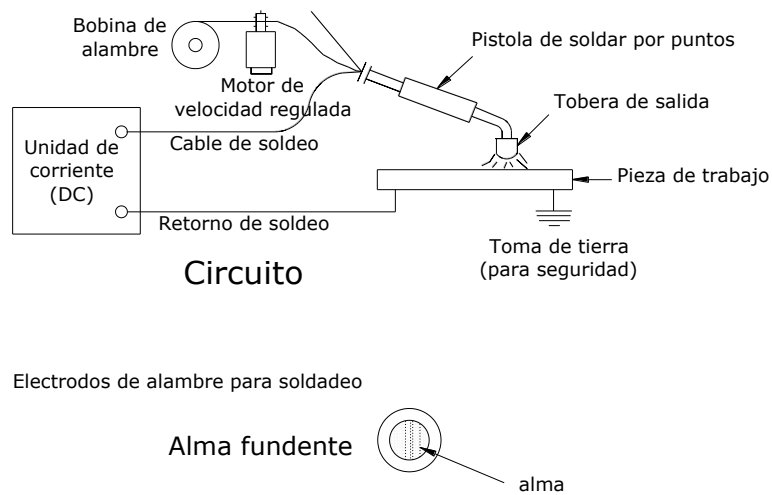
Proceso de soldadura FCAW.
